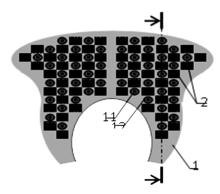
Общий вид устройства (вид сверху) Fig. 3. General view of the device (top view)
